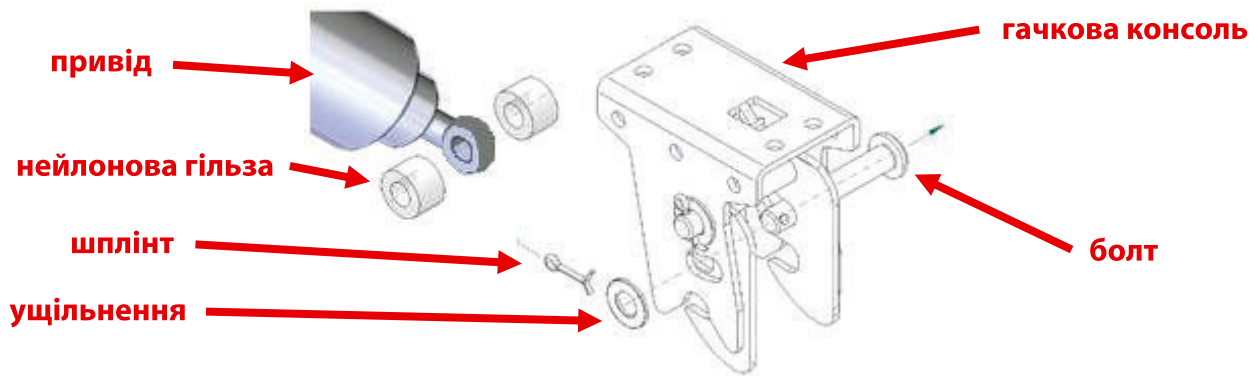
Деталі з'єднання приводу з гачковою консоллю
